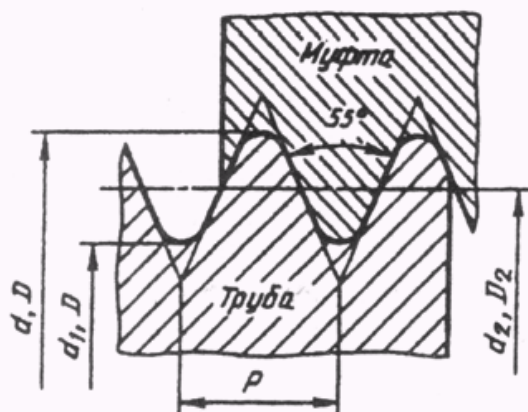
Профиль и основные параметры трубной цилиндрической резьбы
